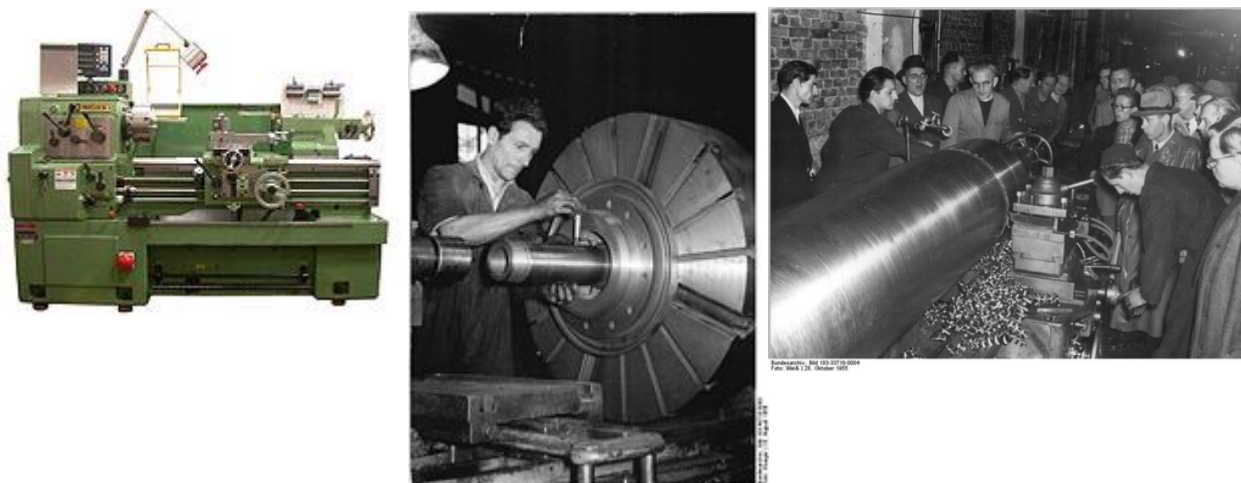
Токарный станок и примеры токарной обработки (точения)
